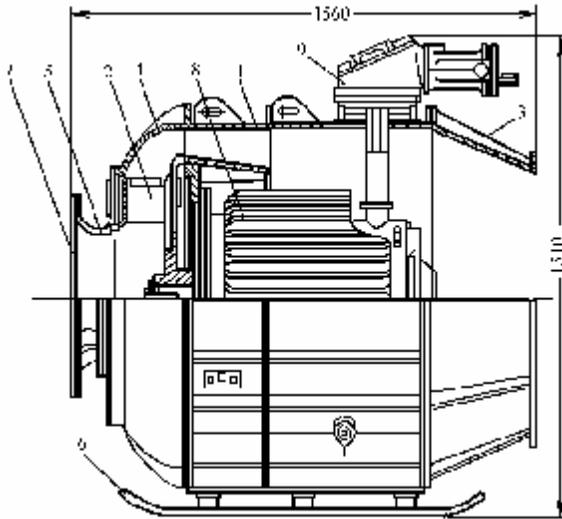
Вентилятор ВЦ-7: 1 – кожух; 2 – рабочее колесо; 3 – выходной патрубок; 4 – передняя часть корпуса; 5 – переходник; 6 – салазки; 7 – коллектор; 8 – двигатель; 9 – кабельный ввод
